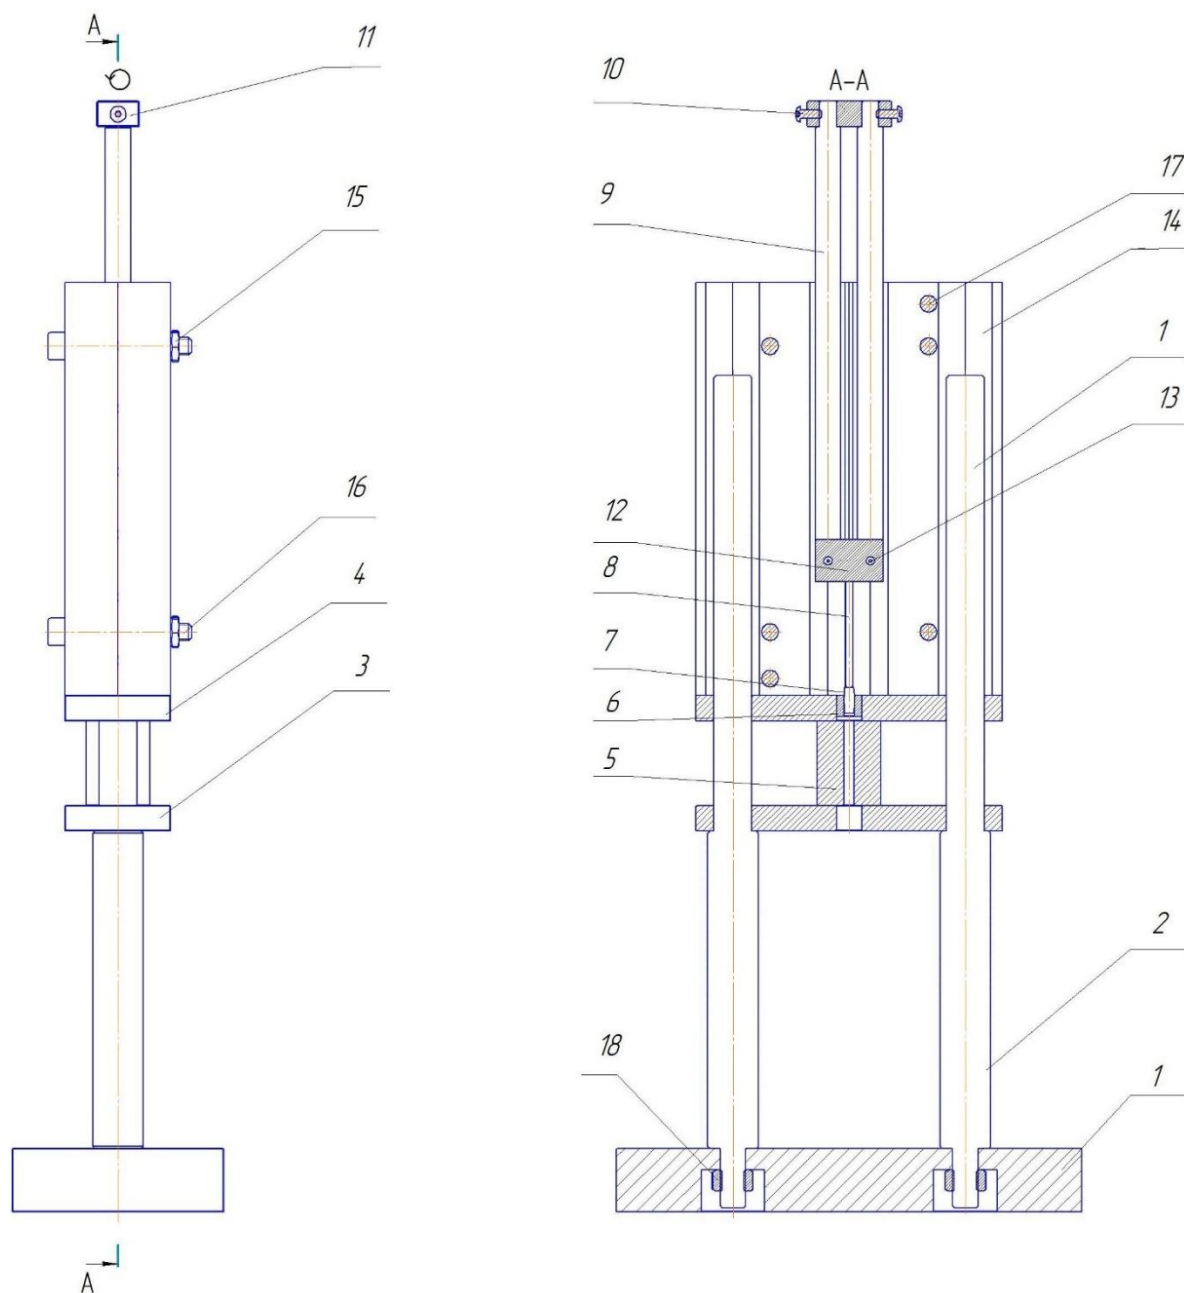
Приспособление для дорнования глубоких отверстий малого диаметра с призматическими направляющими для толкателя
